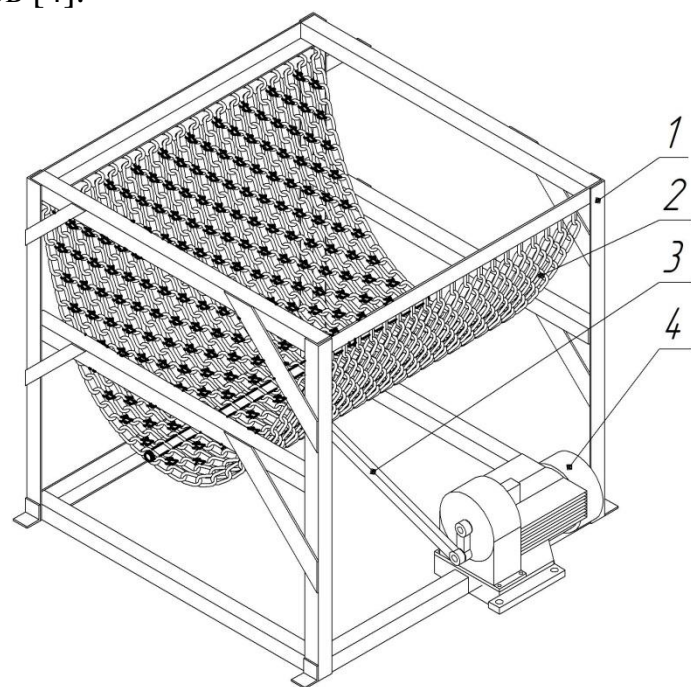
Общий вид цепного измельчителя: 1 – рама; 2 – рабочий орган; 3 – привод; 4 – кривошипно-шатунный механизм
